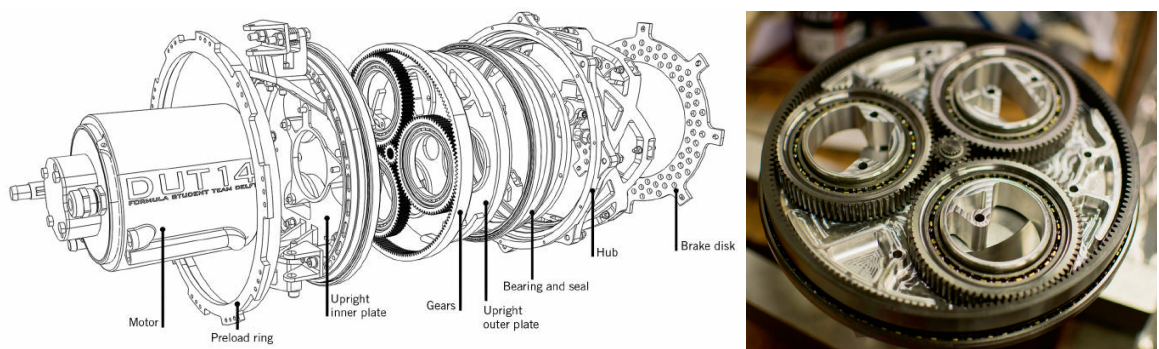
Conjunt motor transmissió explosionat del DUT14 (esquerra). Interior del reductor del DUT14 (dreta).
